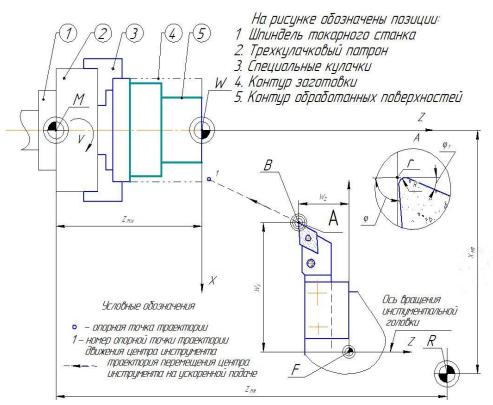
Схема координат станка и привязка системы отсчета к станку, инструменту и детали
